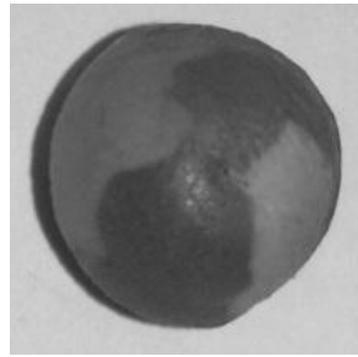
Шар полученный методом осадки в калибр со сферической поверхностью из разноцветного пластилина
